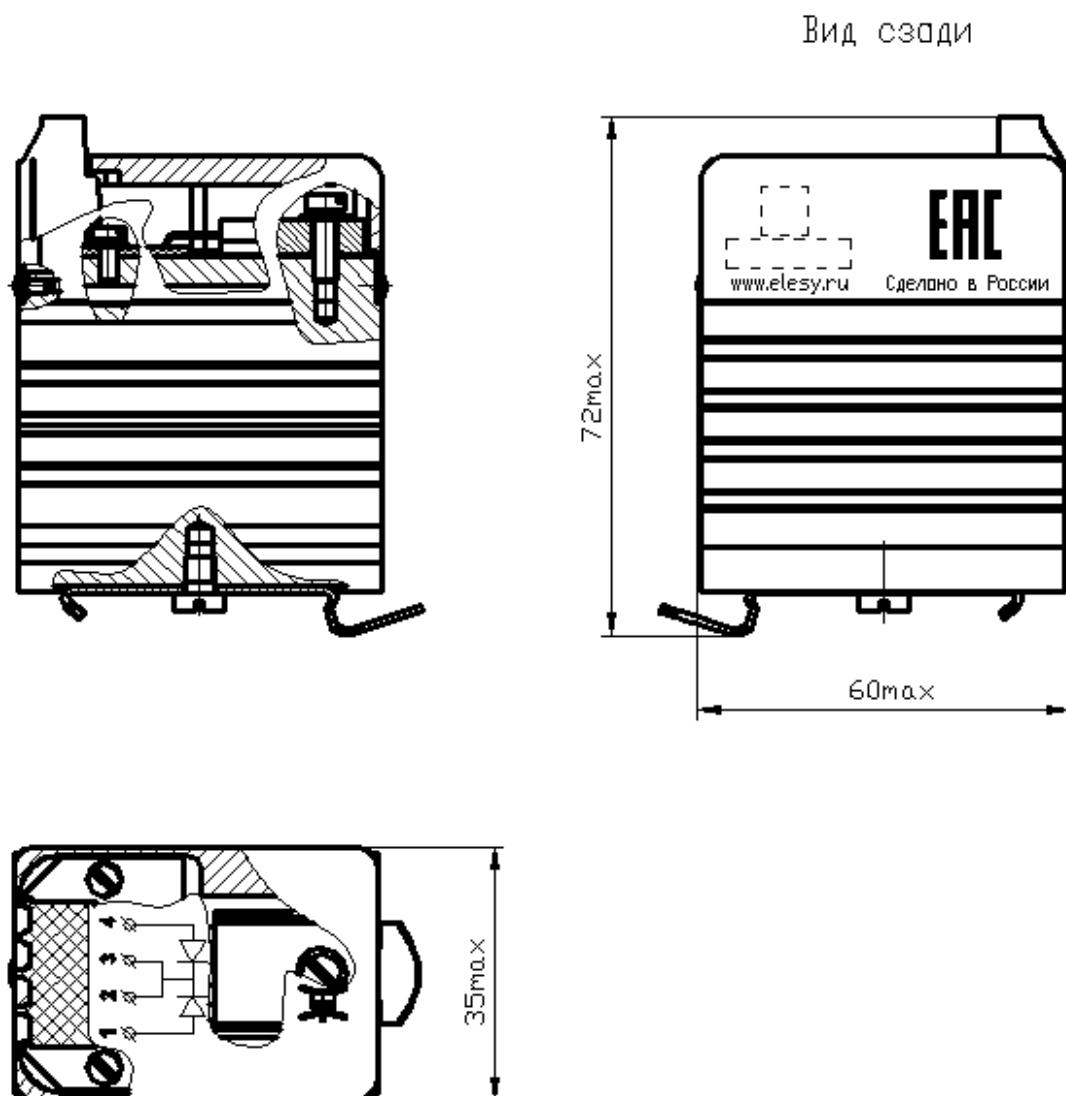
Габаритный чертеж модуля EF R 24DC/24DC-20 С
